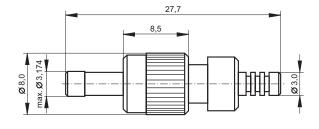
F-SMA Steckverbinder mit Rändelmutter
